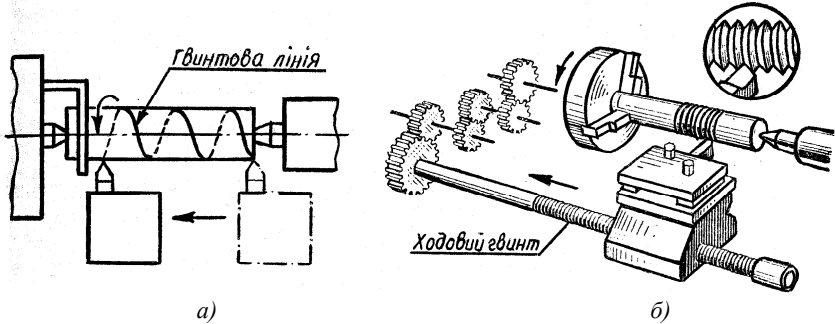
Схема створення гвинтової лінії на циліндричному валику (а) і схема нарізання різьби на токарному верстаті (б)
